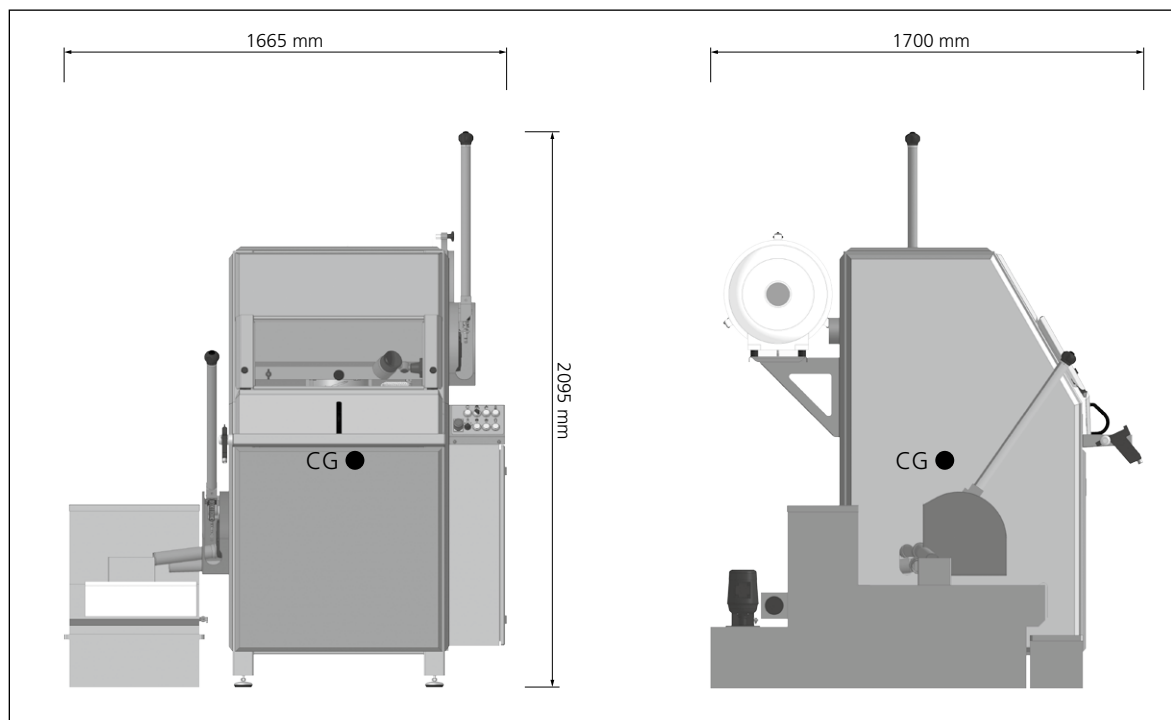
Dimensiones en mm y centro de gravedad (CG) de la máquina
